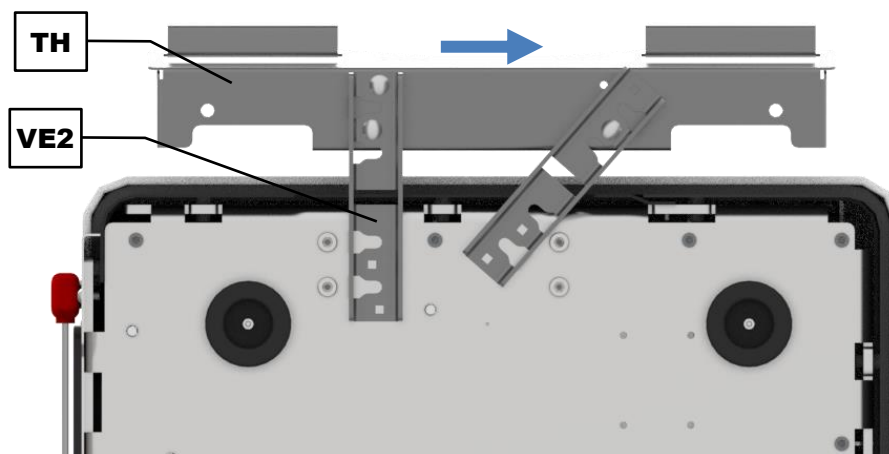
Приспособление для транспортировки — освобождение из крепления
